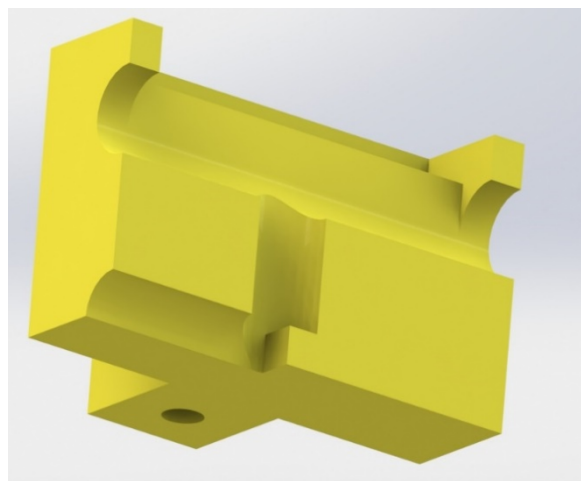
Vista em corte do suporte para componentes do transdutor de caudal
